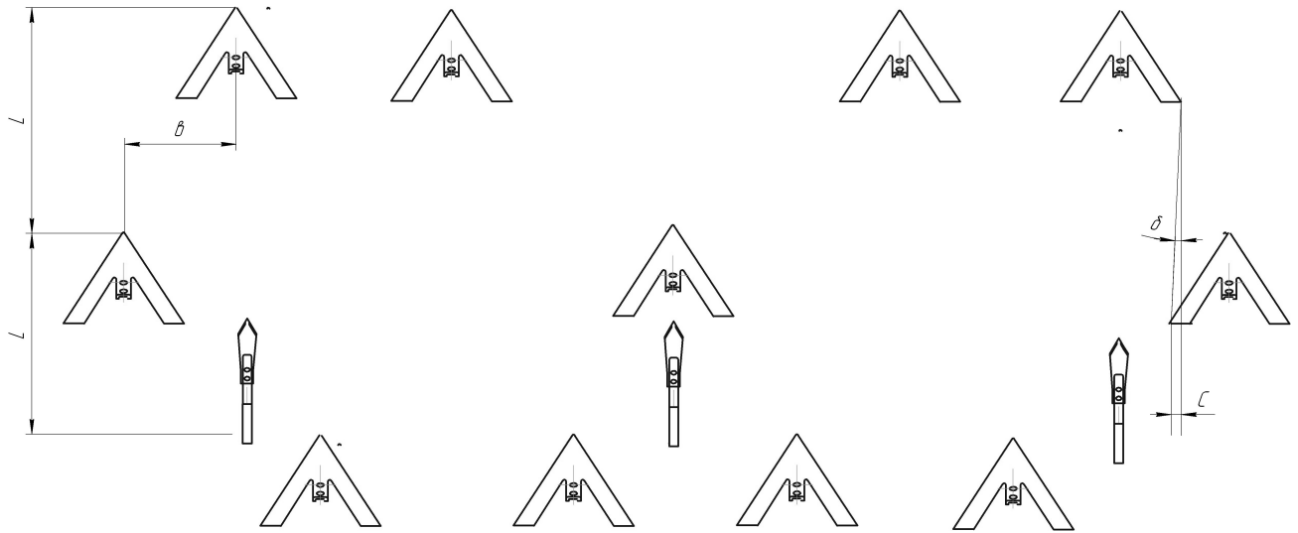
Схема розташування робочих органів на рамі культиватора
